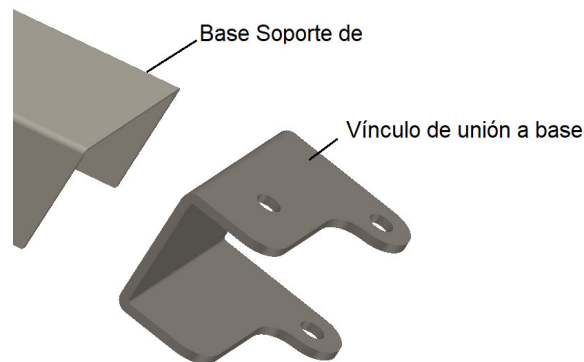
Soldadura del vínculo de unión a base.
